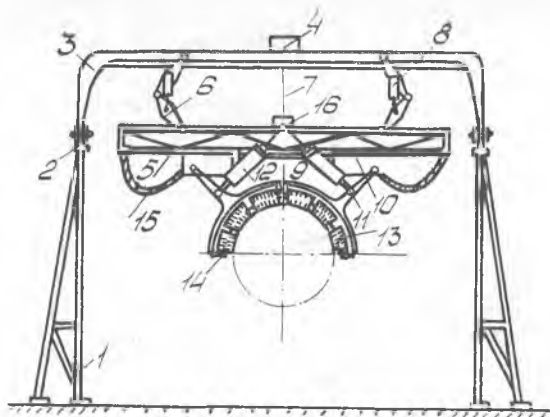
Устройство для мойки верхних поверхностей ЛА (фюзеляжа)
